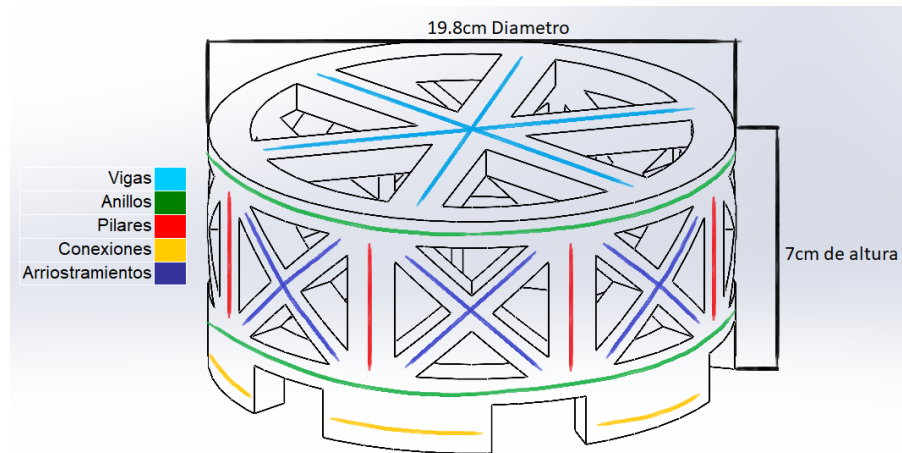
Dimensiones de la base cilíndrica y elementos estructurales.
